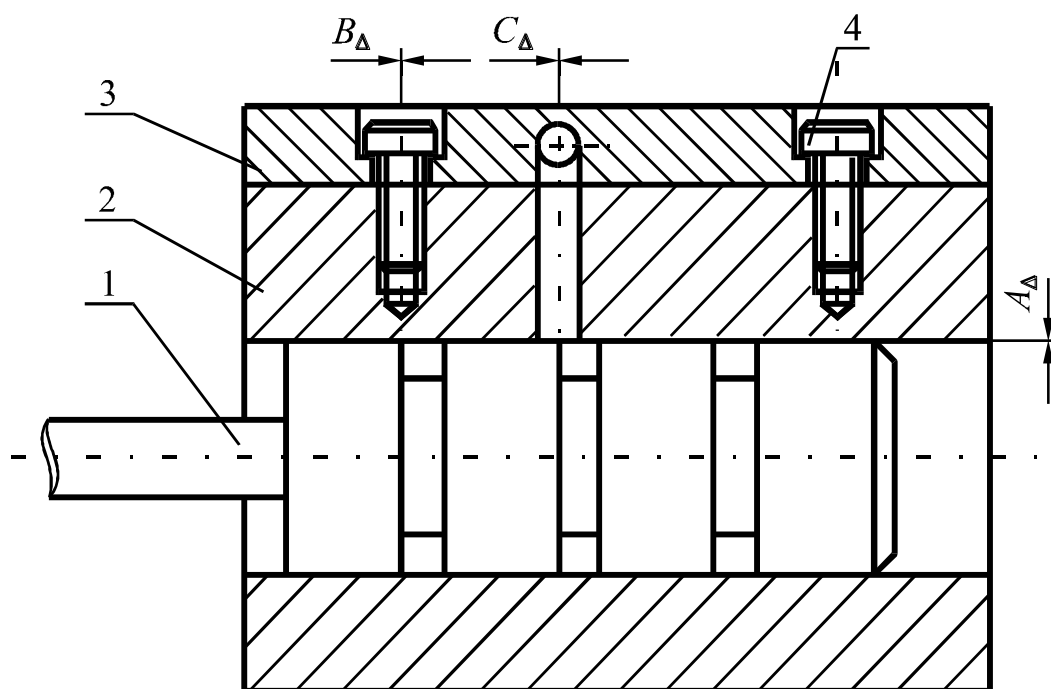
Конструкция золотникового устройства: 1 – золотник; 2 – корпус золотника; 3 – крышка; 4 – крепежные болты (A_{Δ} – зазор, ограниченный посадкой по рабочей поверхности золотника, C_{Δ} – несовпадение осей каналов в крышке и в корпусе золотника, B_{Δ} – несовпадение осей крепежного отверстия в крышке и оси резьбового отверстия в корпусе золотника)
